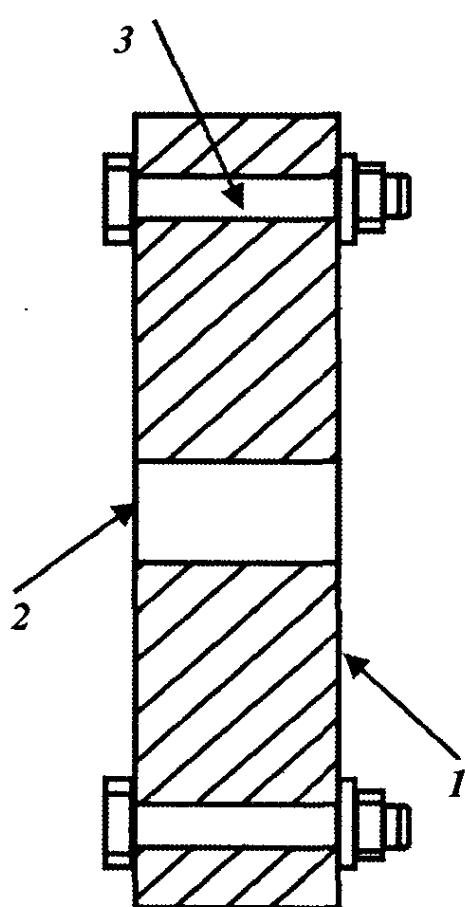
Шлифовальный круг (вид сбоку): 1 — шлифовальный круг; 2 — центральное отверстие; 3 — болт M8 с продольным пропилом.
